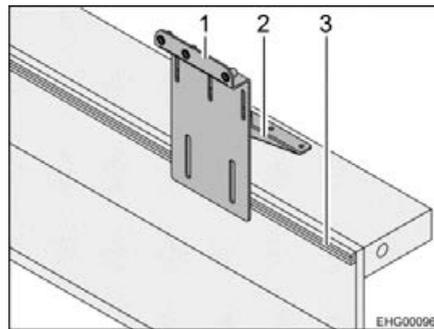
Ersatzradhalterung (an Verzurrutsche)
